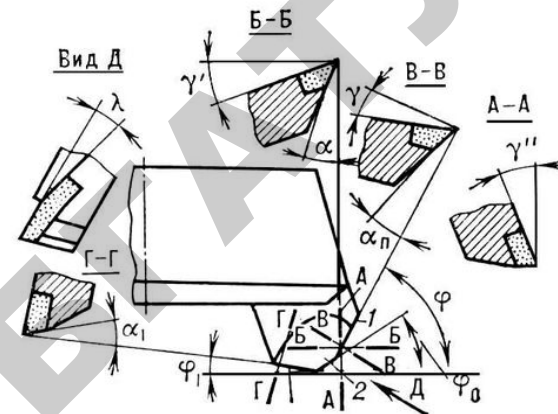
Геометрические параметры режущей части торцевой фрезы:
